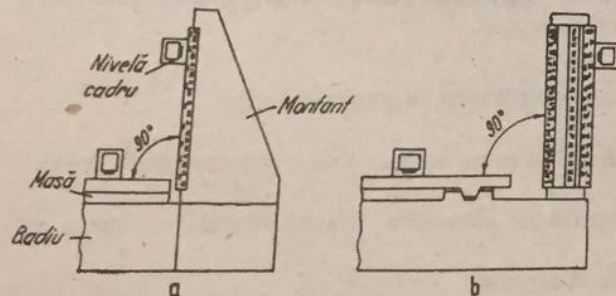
Verificarea perpendicularității montanților: a - în plan longitudinal; b - în plan transversal.
